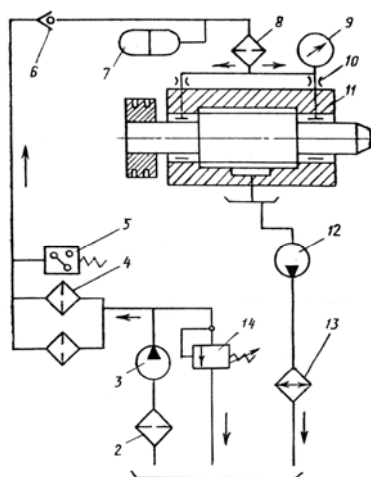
Схема смазочной системы гидростатических опор шпинделя металлорежущего станка:
